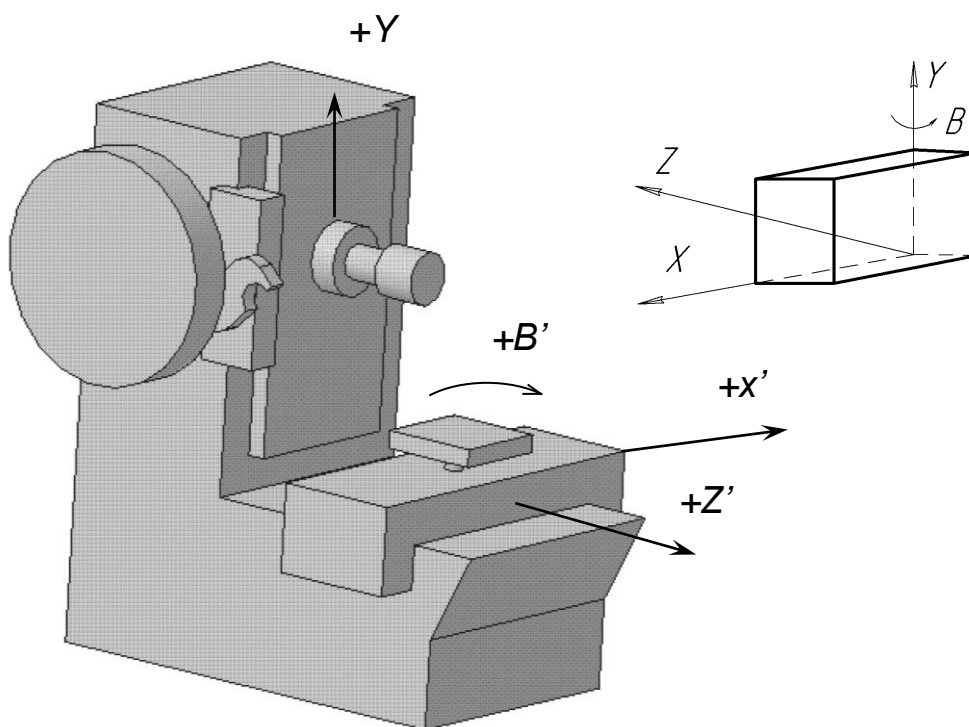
Общий вид многоцелевого станка модели 6904BMФ2
